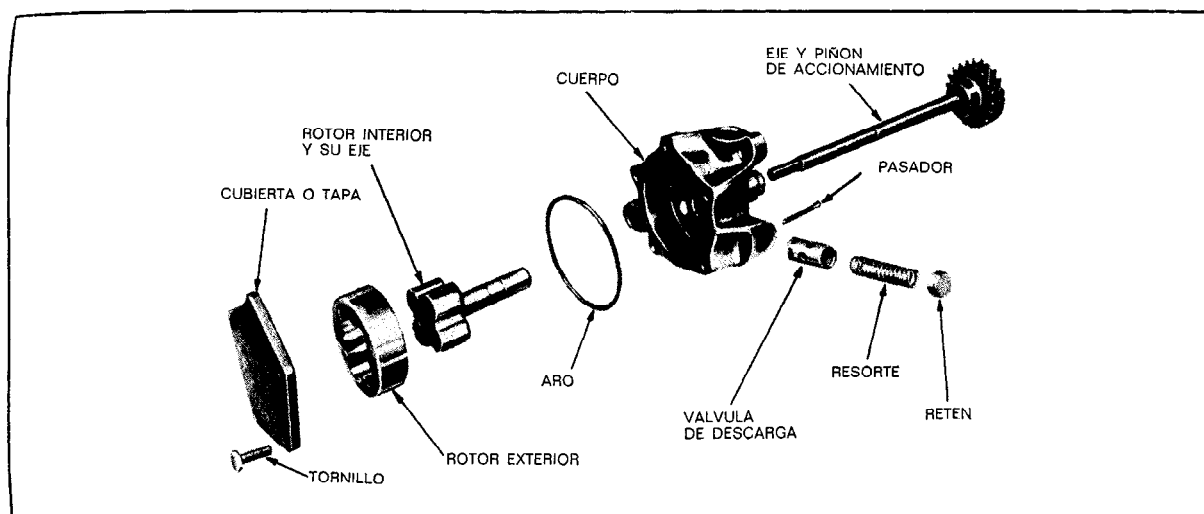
Despiece de una bomba de engrase de rotor (Dodge Division of Chrysler Motors Corporation).
